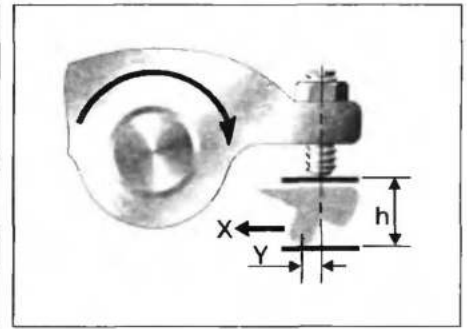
Смещение точки контакта опоры коромысла с торцом клапана: h — подъем клапана; y — смещение; x — направление бокового усилия на стержне клапана
